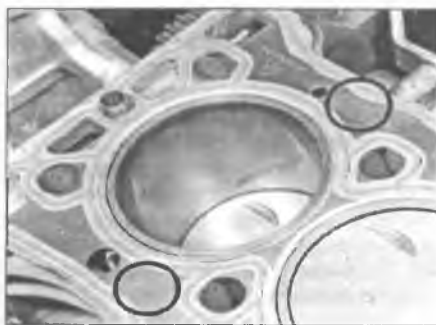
таким образом, чтобы маркировка TOP (ВЕРХ) была сверху, а стрелка FRONT (ПЕРЕД) была направлена к ремню газораспределительного механизма
